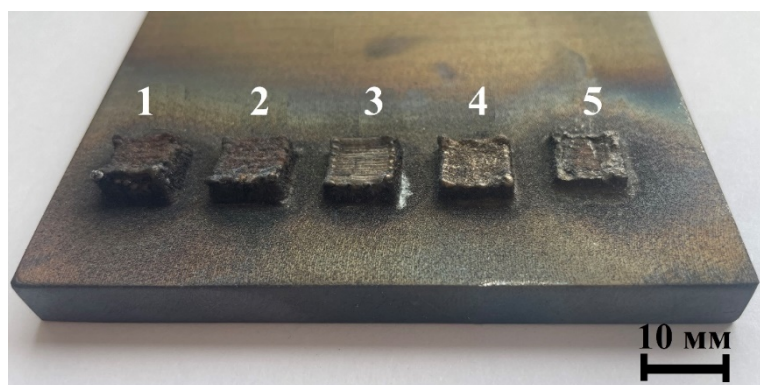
Внешний вид трехмерных образцов наплавки
